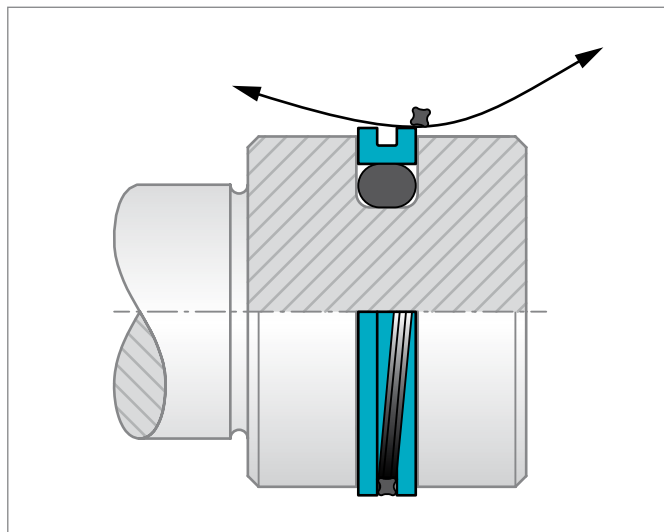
Einbau des Quad-Ring® in AQ-Seal® für Kolben
